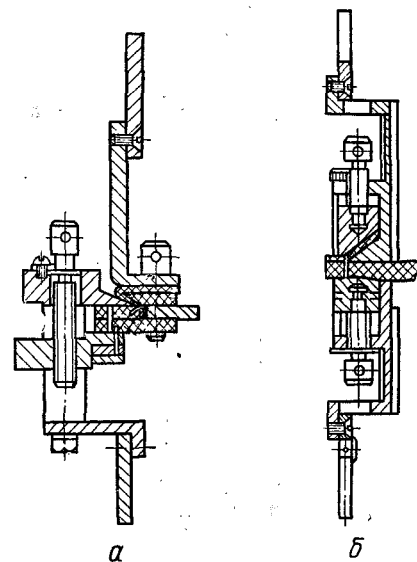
Приспособления к разрывной машине для отрыва ранта от стельки (а) и подошвы от ранта (б)
